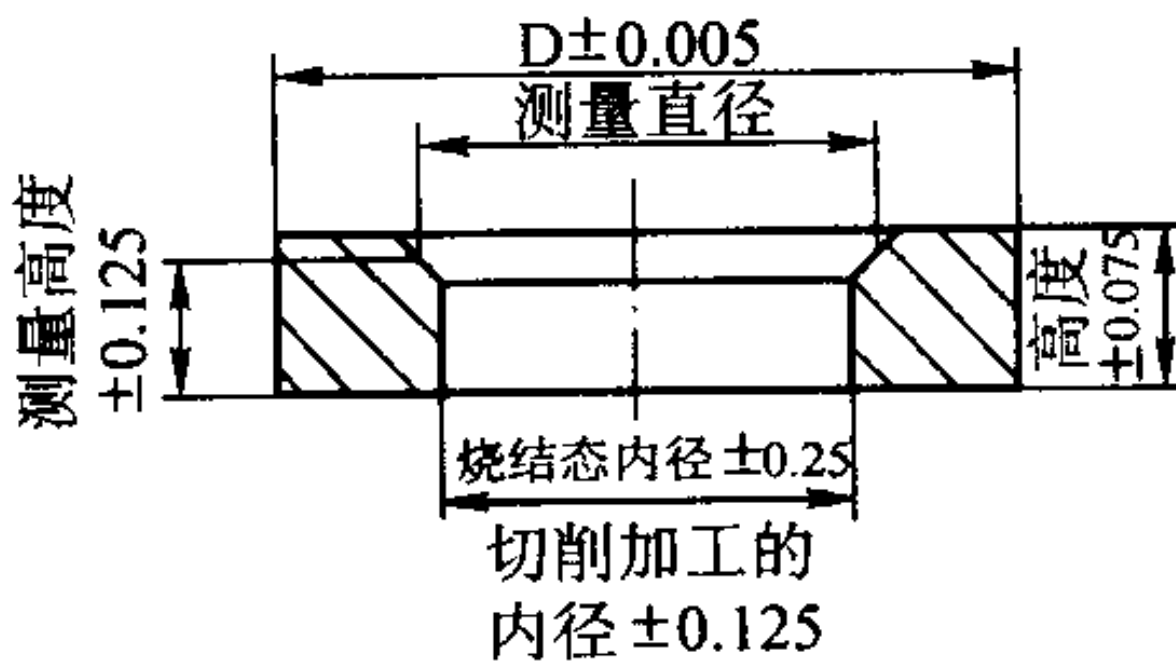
阀座圈的典型形状与尺寸公差
